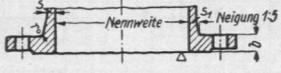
Flansch mit Eindrehung für Runddichtung, DIN 2514.
